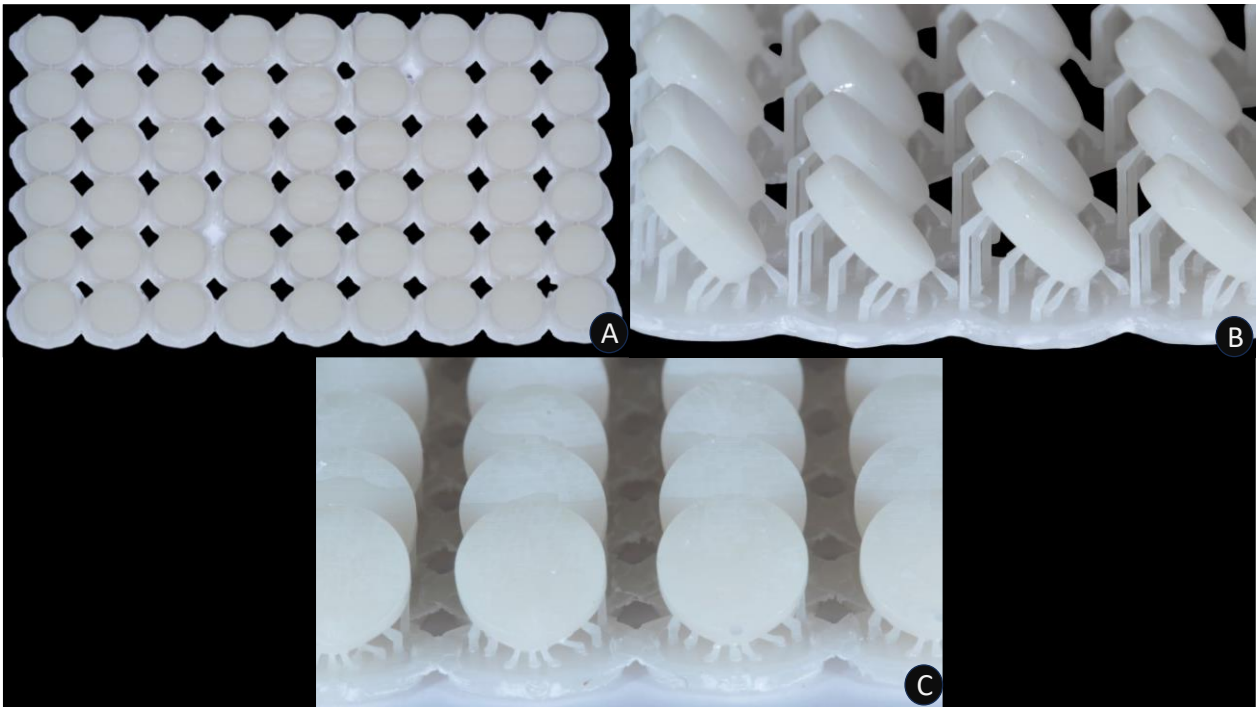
Discos de resina impressos. (A) vista superior. (B) vista lateral. (C) vista frontal.
